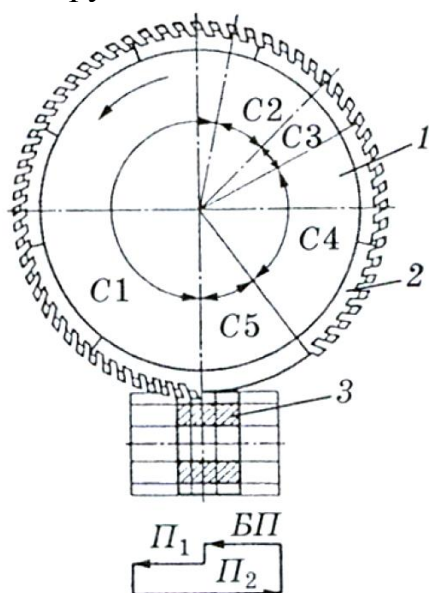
Фрезопроотягивание цилиндрических зубчатых колес: 1 – диск фрезопротяжки; 2 – режущие блоки ; 3 – зубчатое колесо
